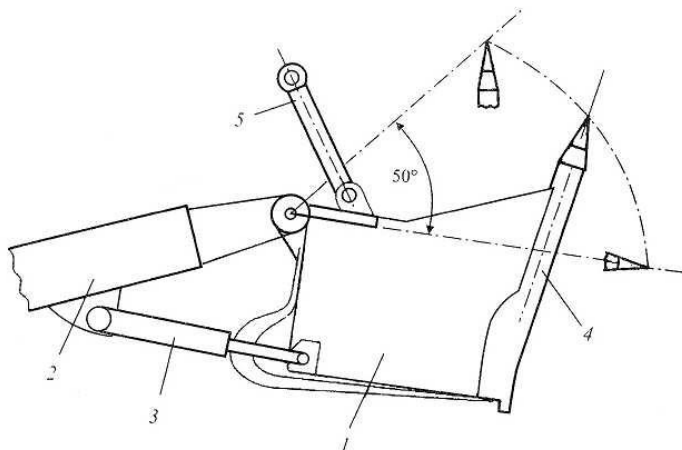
Конструктивна схема ковша активної дії: 1 – ківш; 2 – рукоять екскаватора; 3 – гідроциліндр повороту; 4 – пневмоударник; 5 – підвіска ковша
